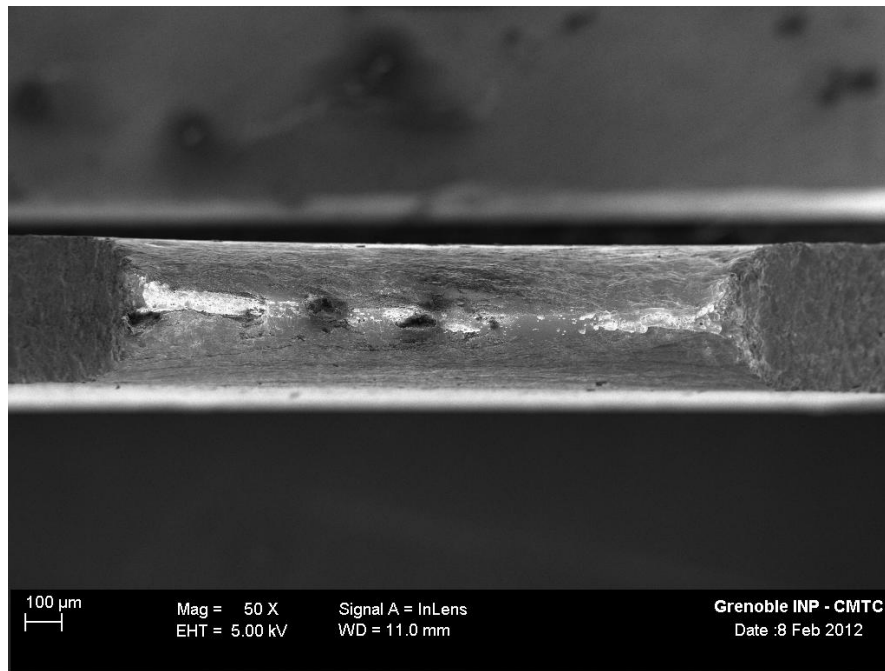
Fractografía de la probeta plana ASTM, con entalle en 90°, de blíster. Se muestra la zona de fractura que se localiza en el entalle.
